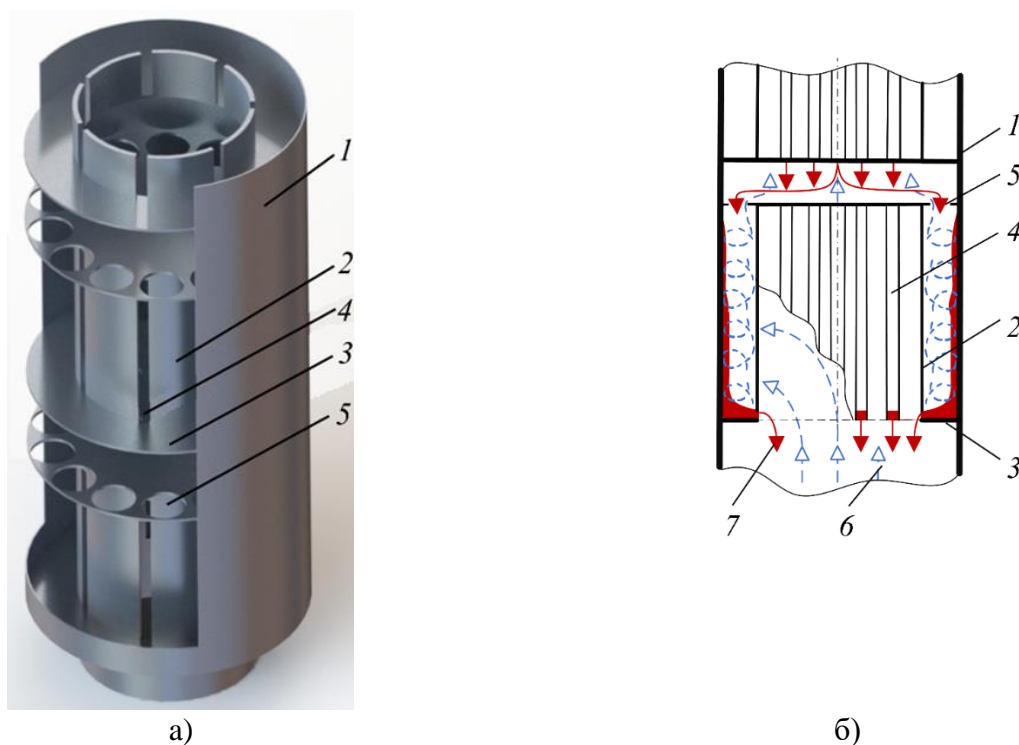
Трехмерный вид с отображением внутренних элементов (а) и принцип работы многоступенчатого вихревого контактного устройства (б): 1 – корпус; 2 – цилиндрический патрубок; 3 – основание; 4 – вертикальные прорезы; 5 – отверстия для парового потока; 6 – паровой поток; 7 – поток жидкости.
